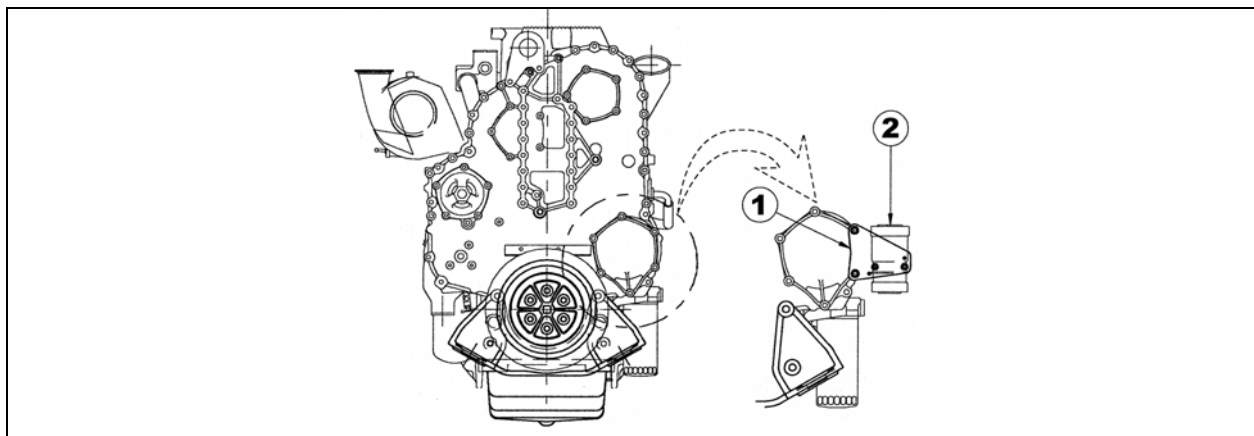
SUPPORT DE LA POMPE À CARBURANT (1), POMPE À CARBURANT ÉLECTRIQUE (2)
